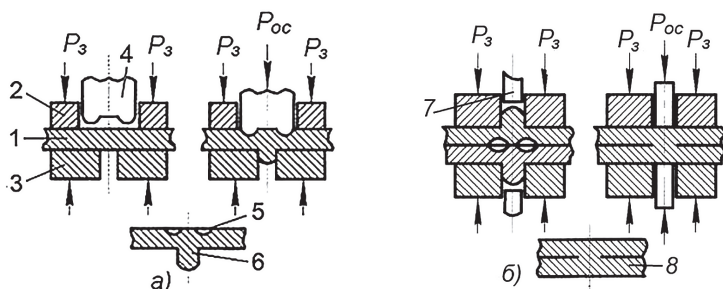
Схема точечной сварки с предварительным (а) и окончательным (б) деформированием
